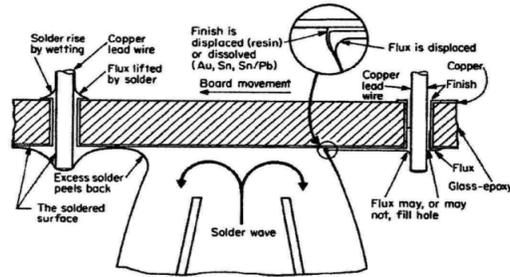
12 – Soldadura por Onda. Fonte: Coombs (2008)
